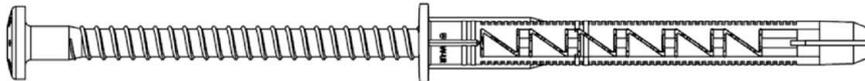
WÜRTH Kunststoff-Rahmendübel W-UR 8x80 mit Pan Head Schraube
